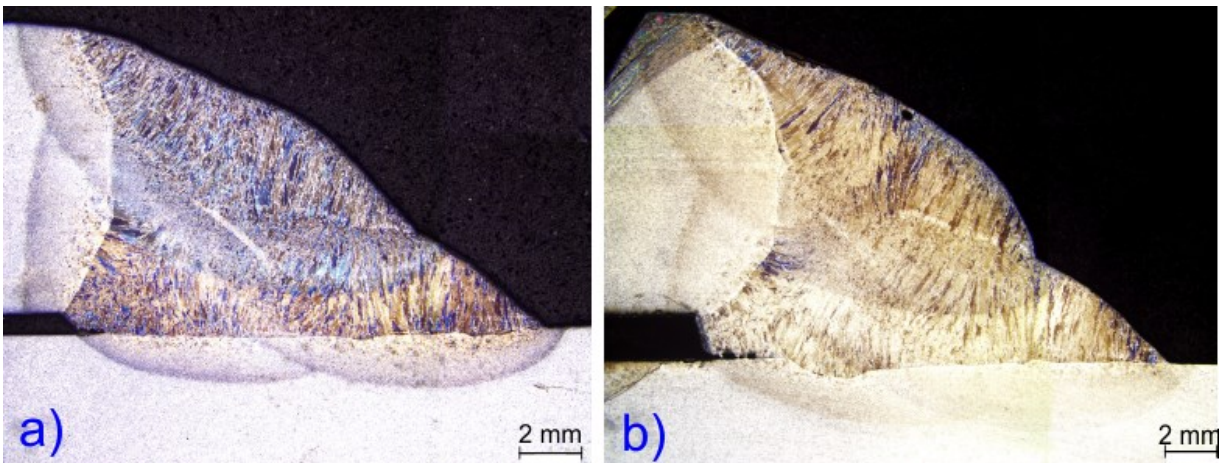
Macrografias da soldagem de dupla-calha com GMAW-P AC. Em a) Sem pré-aquecimento por indução; b) Com pré-aquecimento da calha por indução.
